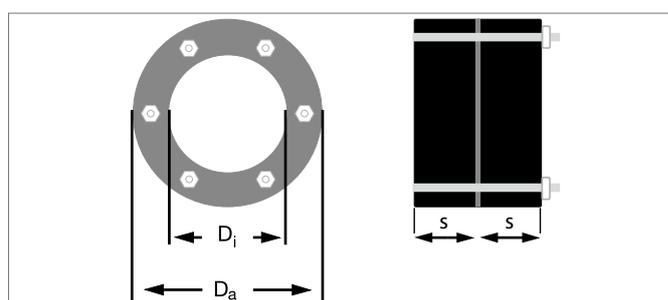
Rappresentazione e dimensioni flangia di tenuta FA 80
